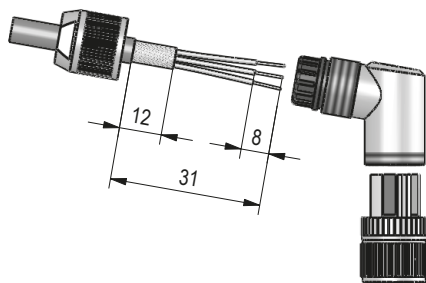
Gegenstecker M12 A-kodiert gewinkelt
